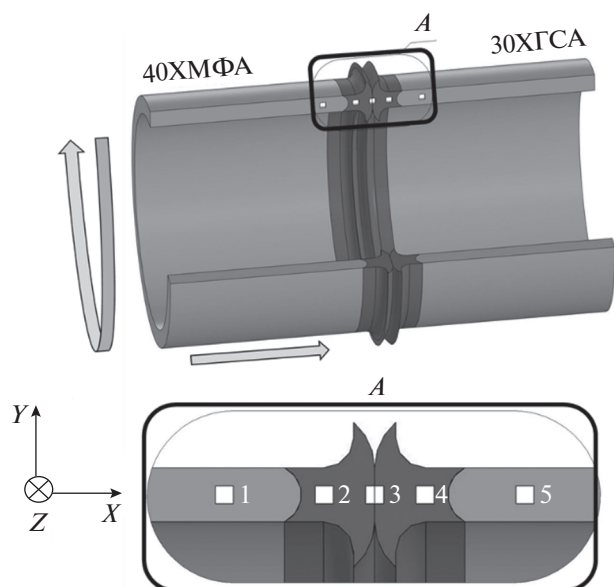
Схема отбора образцов для структурных исследований с указанием используемой при анализе текстуры системой координат (стрелками обозначено направление движения заготовки при сварке); 1, 5 — исходный металл, 2, 4 — зоны термомеханического влияния, 3 — область сварного шва.
